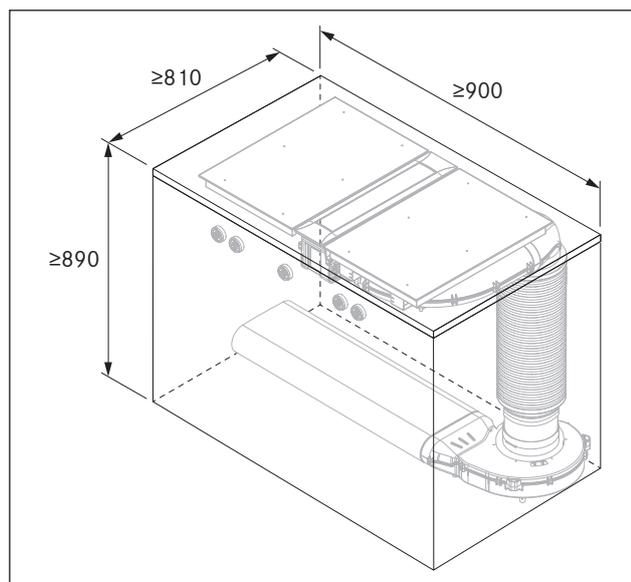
Dimensioni minime di montaggio PKA3/PKA3AB per il montaggio standard
